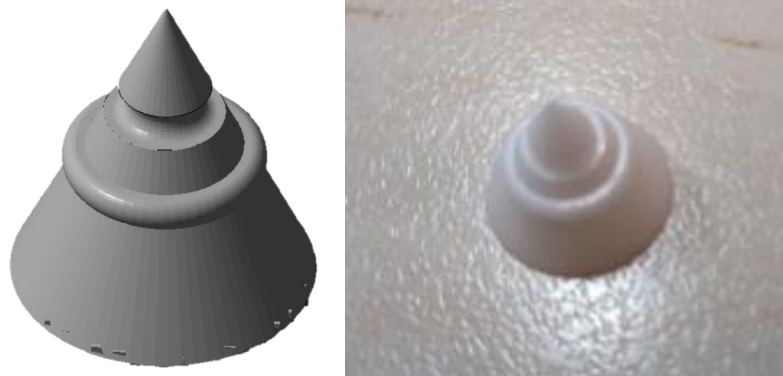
Diseño CAD 3D de la Pieza demo#2 de material cerámico (izquierda). Ejemplo de pieza cerámica fabricada (derecha).
